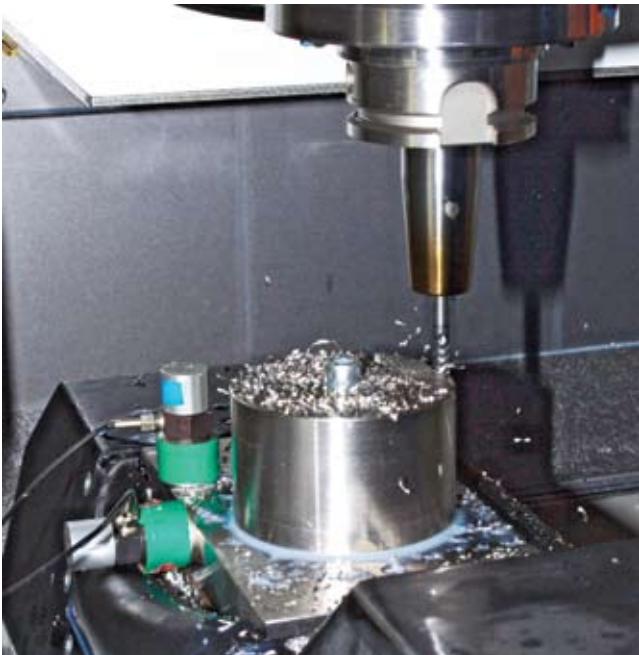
Обработка уступа фрезой, закрепленной в термопатроне
